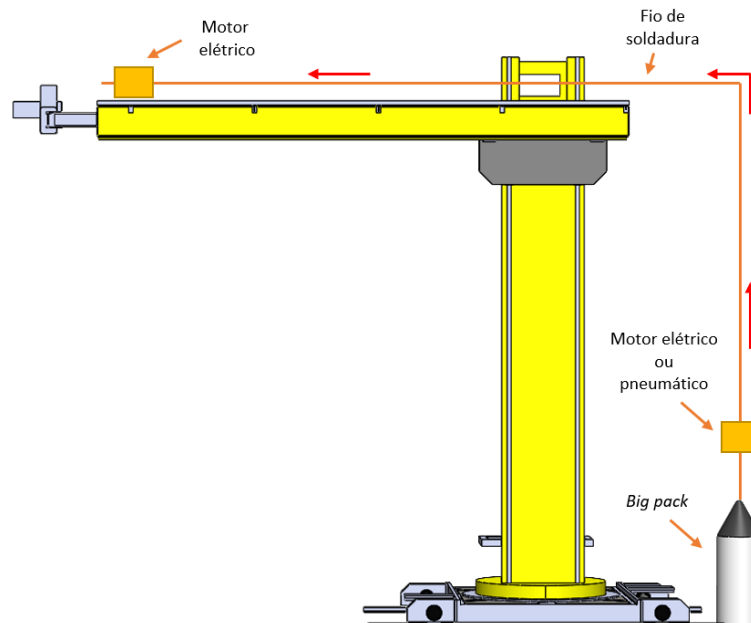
Esquema de transporte do fio de soldadura
